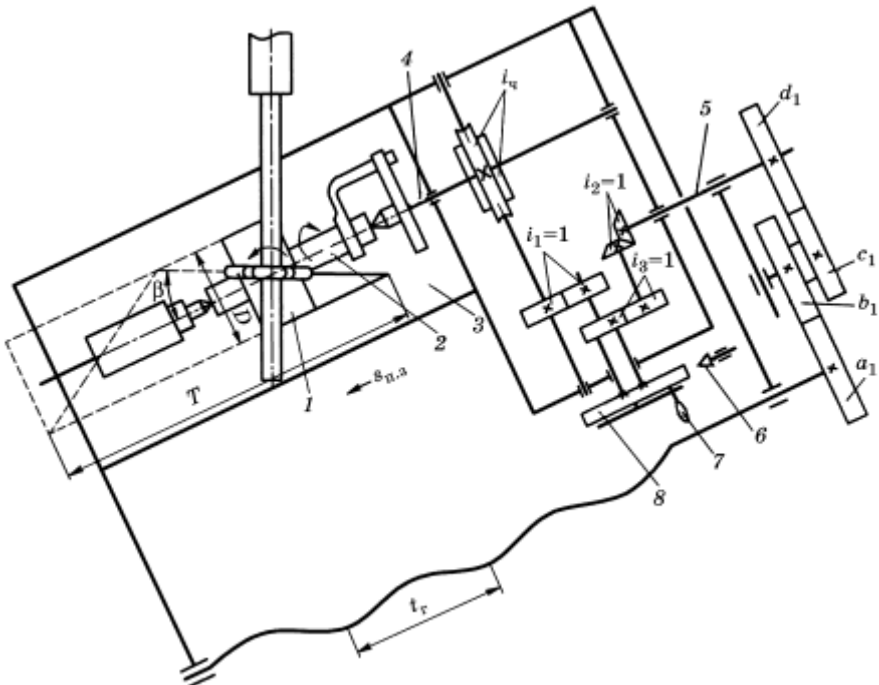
Схема налагодження універсально-фрезерного верстата і ділильної головки на фрезерування гвинтових канавок (косих зубів)
